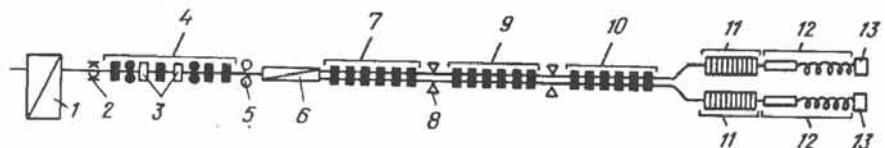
Схема расположения оборудования непрерывного проволочного стана 150:
